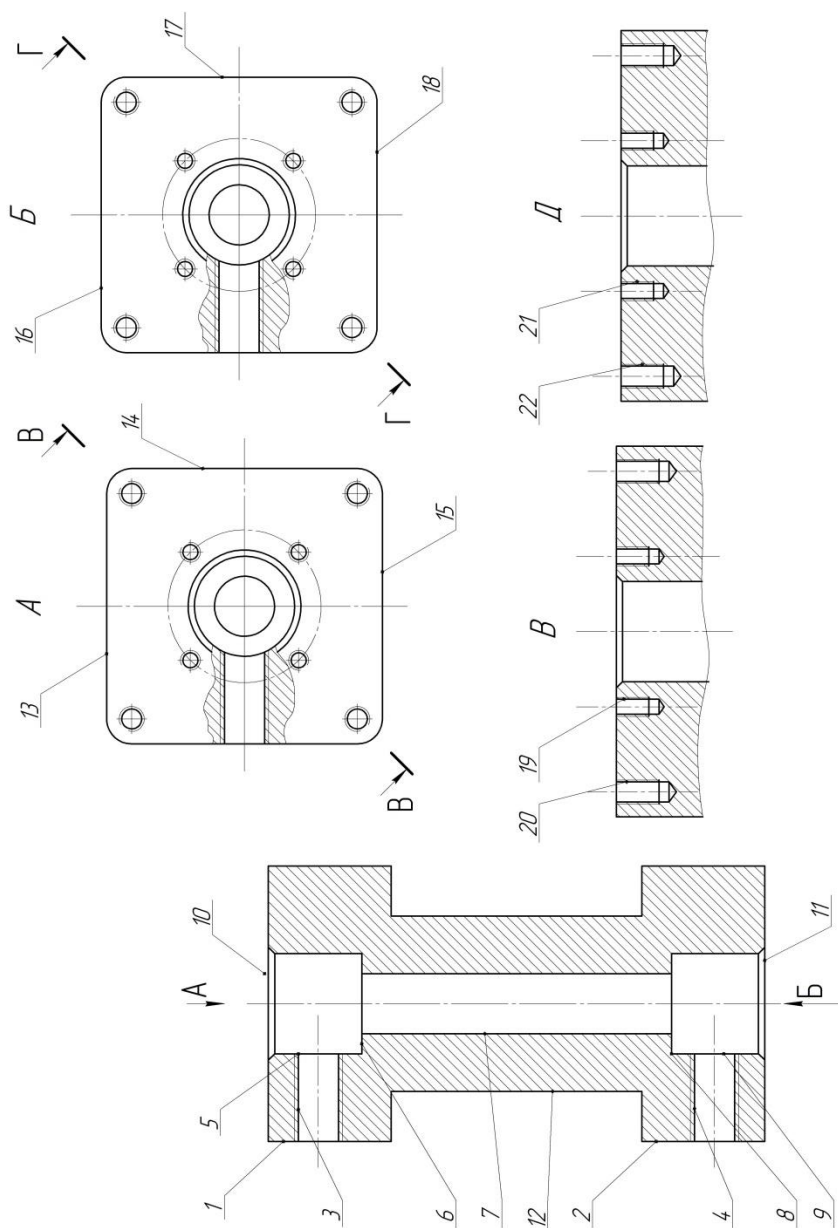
Общий вид детали - «Втулка гидроразветвителя»
